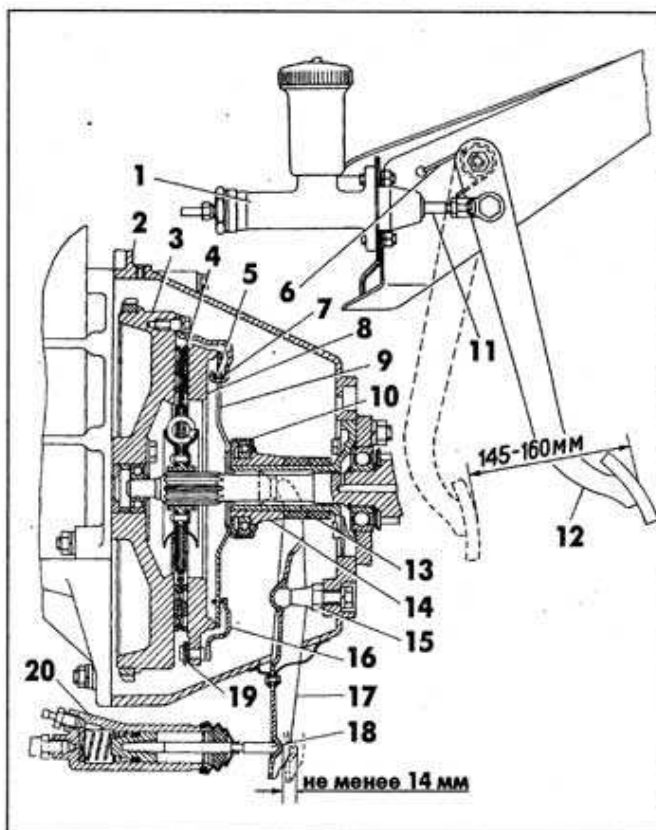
Сцепление диафрагменного типа и привод его выключения: 1 – главный цилиндр; 2 – картер; 3 – маховик; 4 – ведомый диск; 5 и 7 – опорные кольца; 6 – оттяжная пружина педали; 8 – нажимной диск; 9 – нажимная диафрагменная пружина; 10 – подшипник выключения сцепления; 11 – толкатель главного цилиндра; 12 – педаль; 13 – защитные порополоновые кольца; 14 – муфта выключения сцепления; 15 – шаровая опора; 16 – кожух; 17 – вилка выключения сцепления; 18 – толкатель рабочего цилиндра; 19 – соединительные пластины; 20 – рабочий цилиндр
